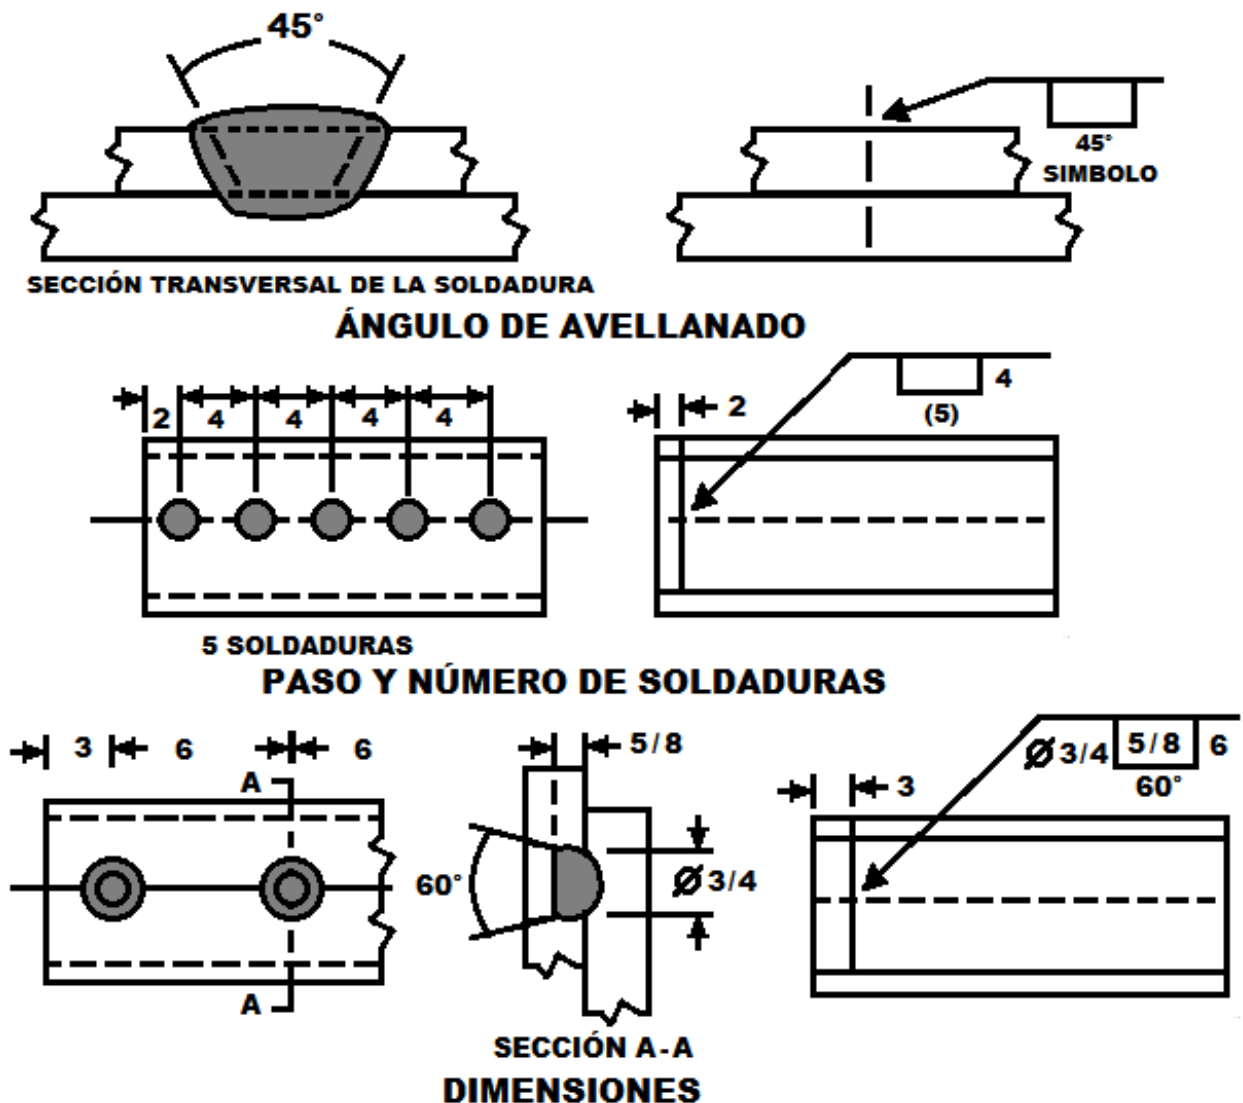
Símbolos de soldaduras de tapón (3, 31)
